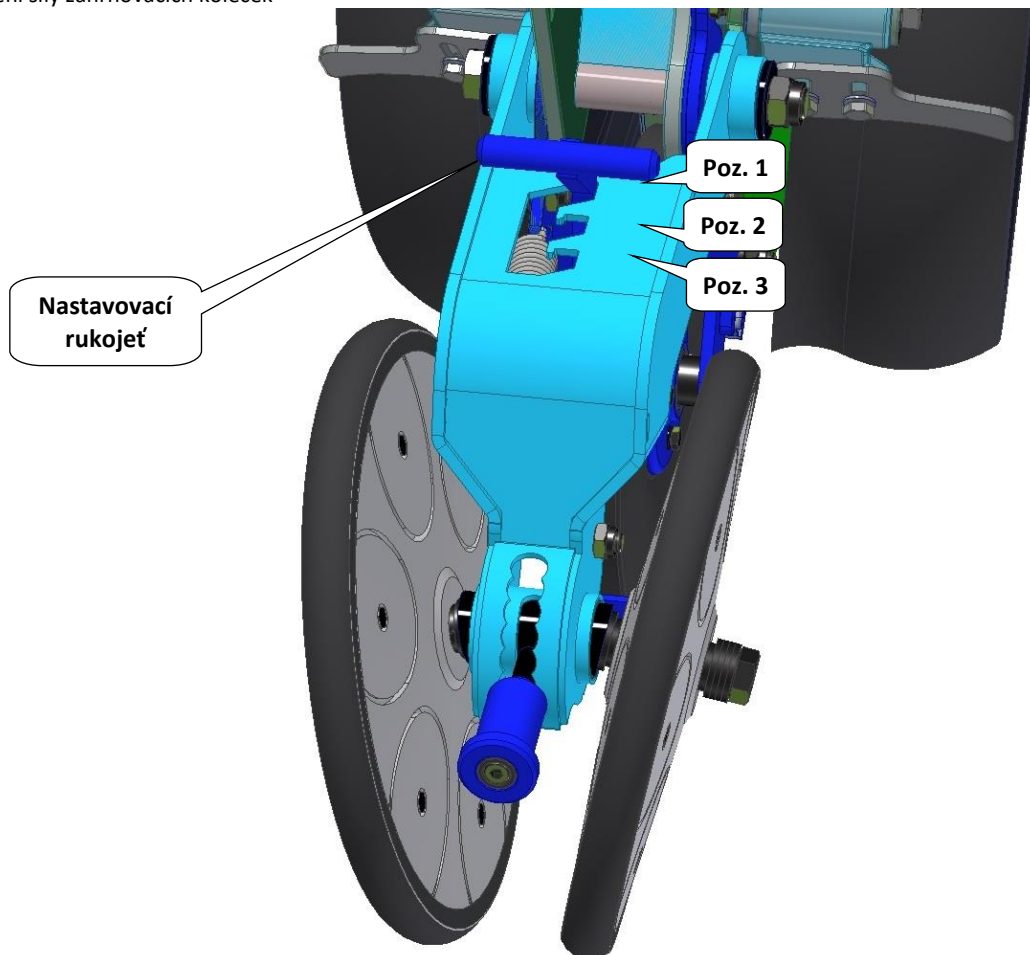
Nastavení úhlu zahrnovacích koleček
